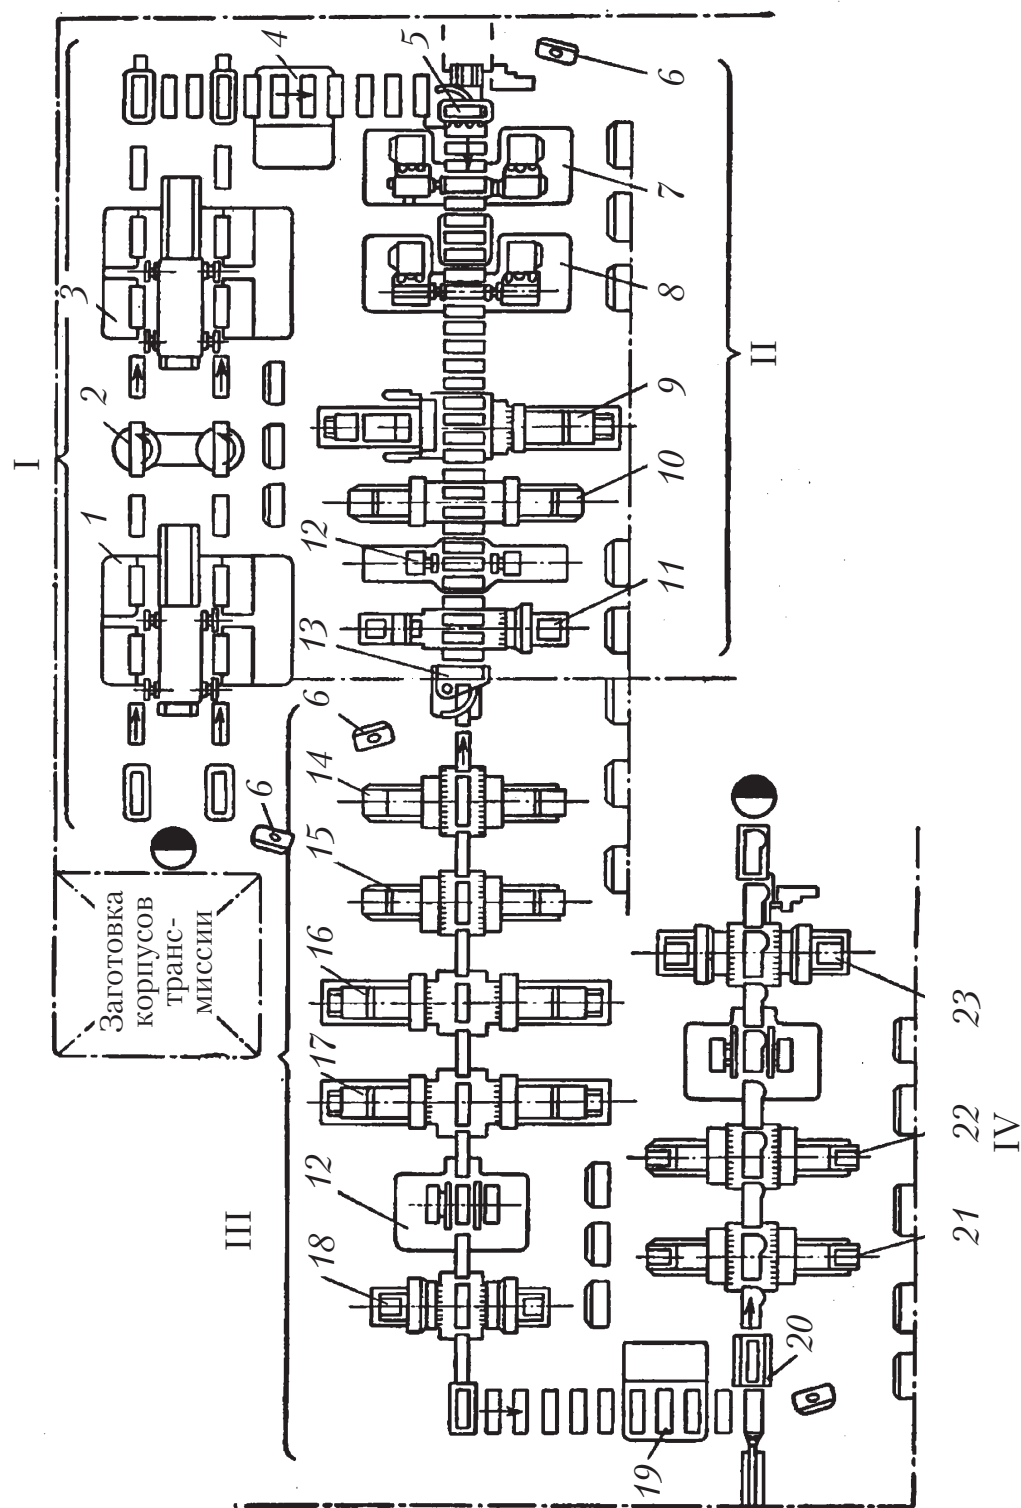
Схема автоматической линии для обработки корпуса трансмиссии трактора:
